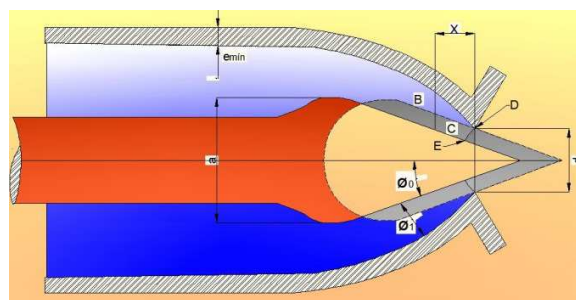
Dimensiones de un inyector de una turbina Pelton. [16]
